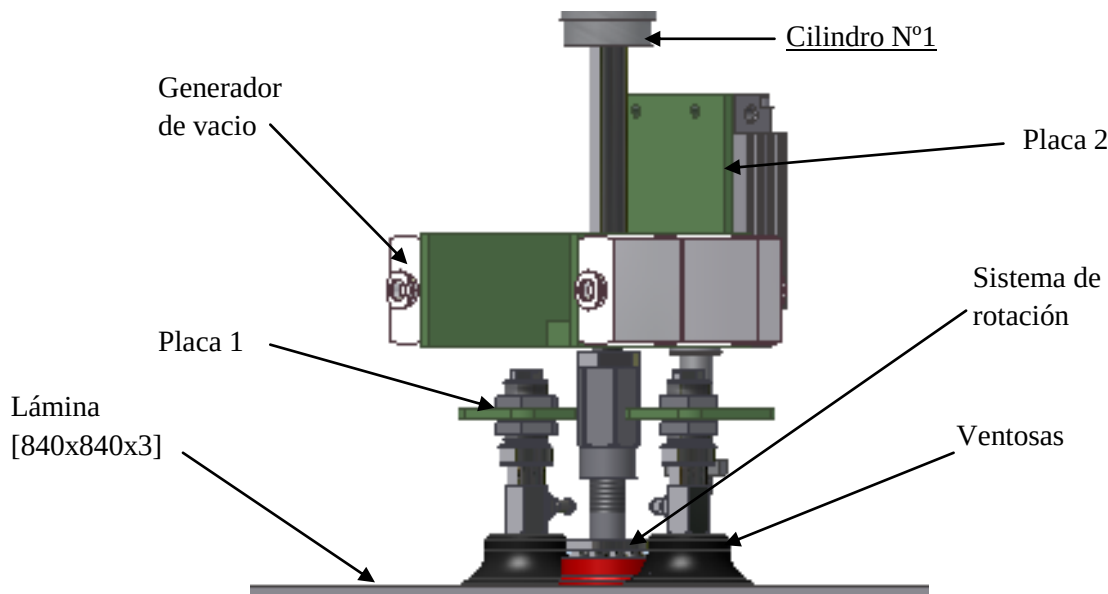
Elementos a levantar por el Cilindro N°1.
